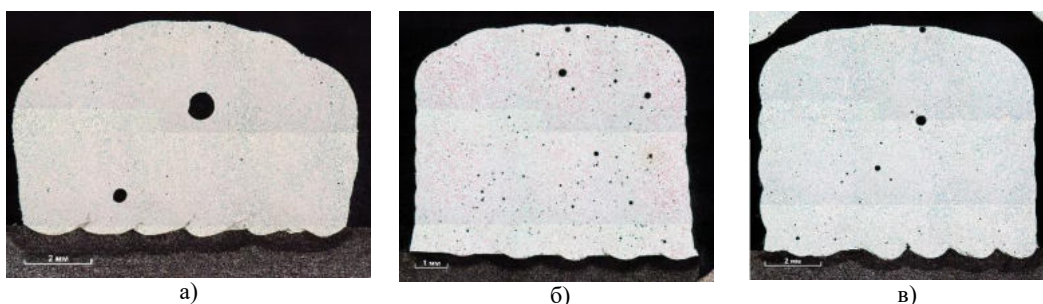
Шлифы образцов сплава ПР-ХН52К11МТЮ: а) – образец 12; б) - образец 16; в) - образец 20
